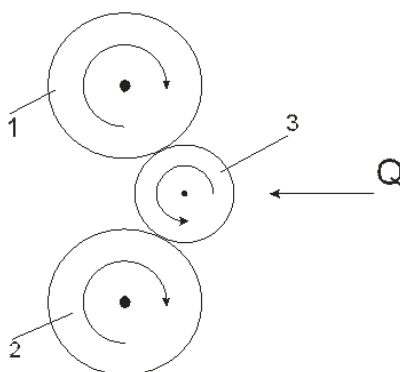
Поперечная прокатка: 1,2 – верхний и нижний валки; 3 – заготовка; Q – удерживающая сила
